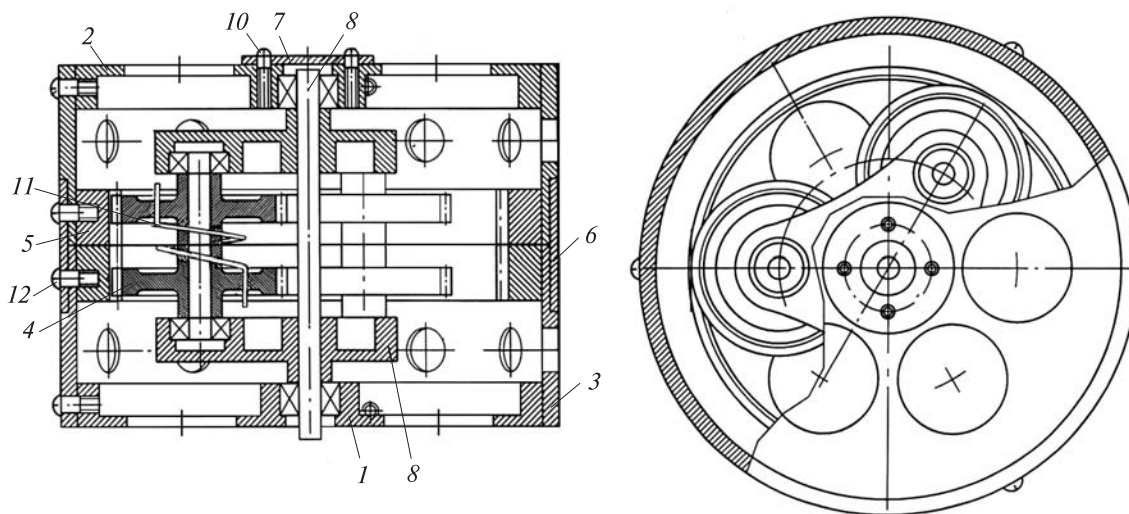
Схема модульного узла трения «зубчатая передача»: 1, 2 — торцевые крышки, 3 — цилиндрический корпус, 4 — сателлитные колеса, 5 — ведомое колесо, 6 — переходное кольцо, 7 — крышка, 8 — водила, 9 — приводной вал, 10 — винт, 11 — цилиндрические пружины кручения, 12 — стопорный винт
